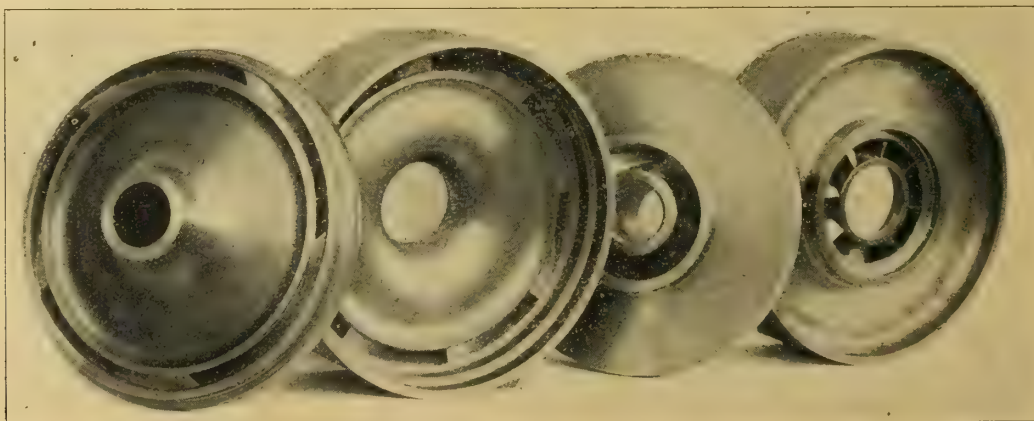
Leit- und Schaufelräder der Hochdruckzentrifugalpumpe, Patent Kugel-Gelpke. In der Ausführung von Escher, Wyß & Co. in Zürich.
